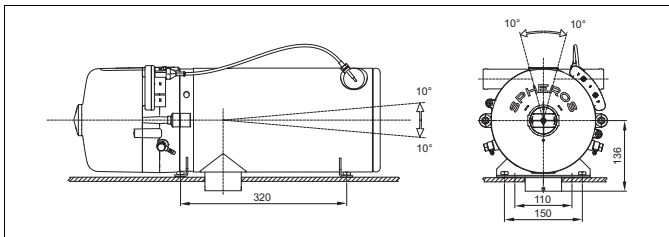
Габаритные размеры подогревателя Thermo E 200/320
